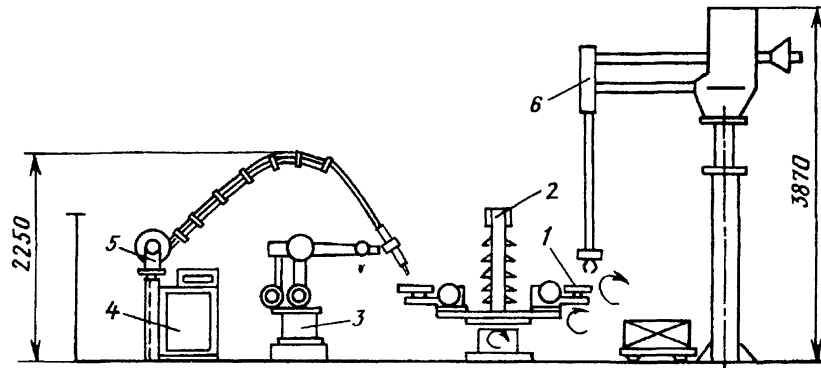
Типовое роботизированное рабочее место для дуговой сварки на базе универсального робота ТУР10
